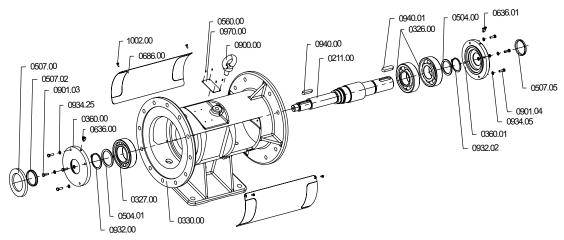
Обзор деталей: опора подшипника для двигателей типоразмера 180 и выше
